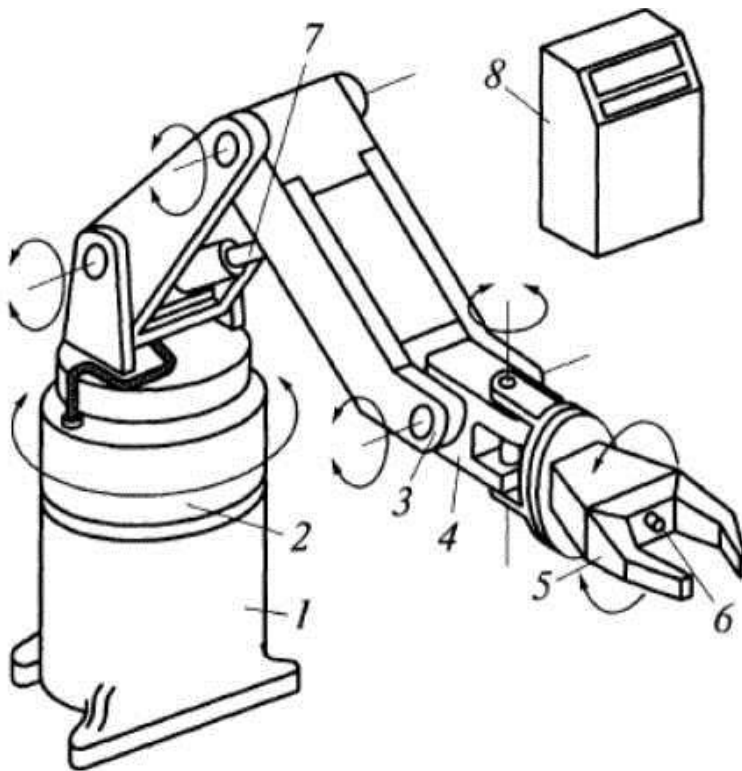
Конструкція промислового робота (1 – опорна конструкція (основа); 2 – колона; 3 – рука маніпулятора; 4 – кисть; 5 – робочий орган (захват); 6 – датчик зворотного зв’язку; 7 – привод руки; 8 – блок керувального пристрою з пультом)
